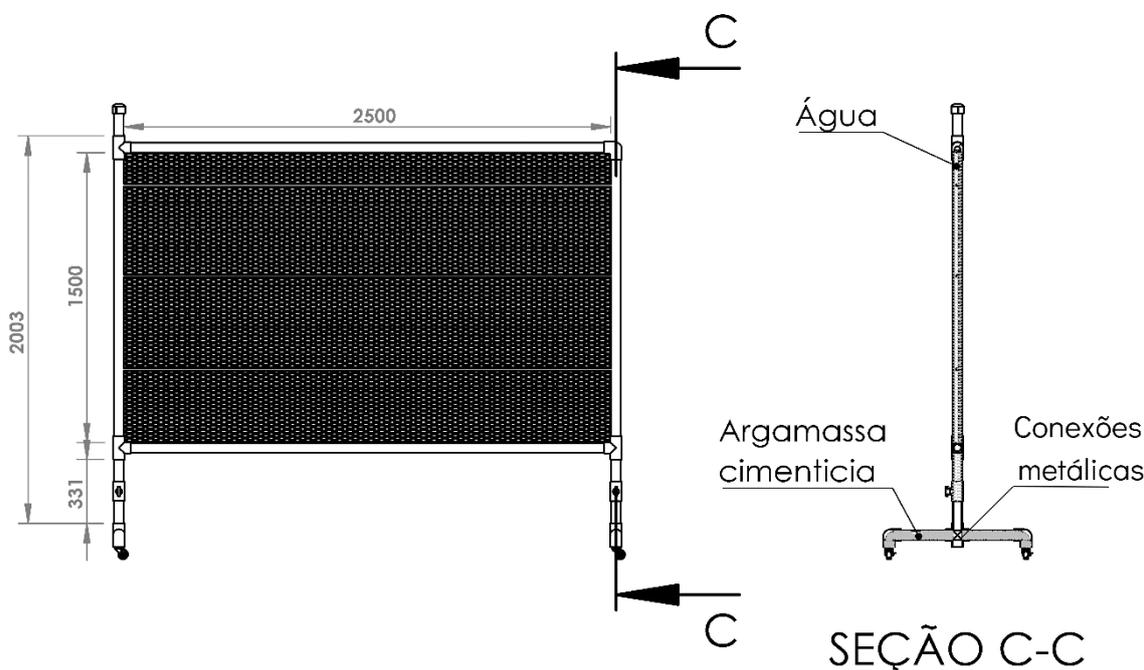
Vista frontal e seccionada da estrutura com dimensões em milímetros
